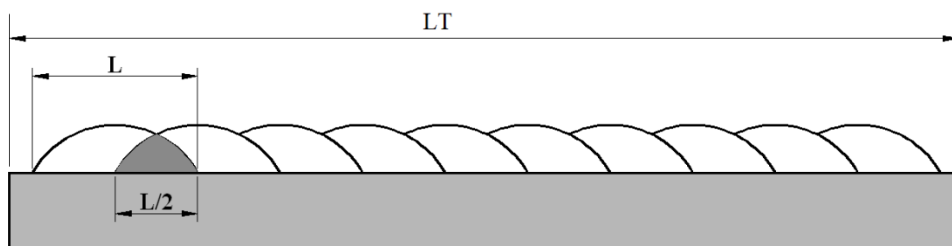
Esquema de soldagem do revestimento com largura total (LT).
